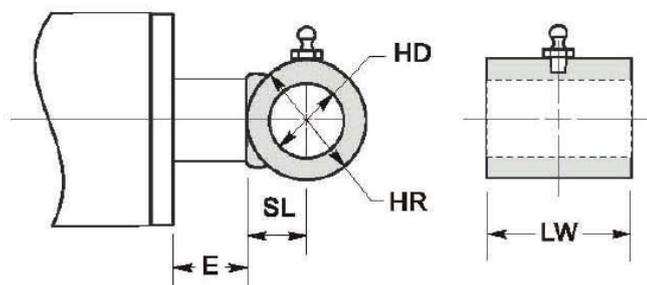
Монтажные крепления штока типа «Широкая проушина»
